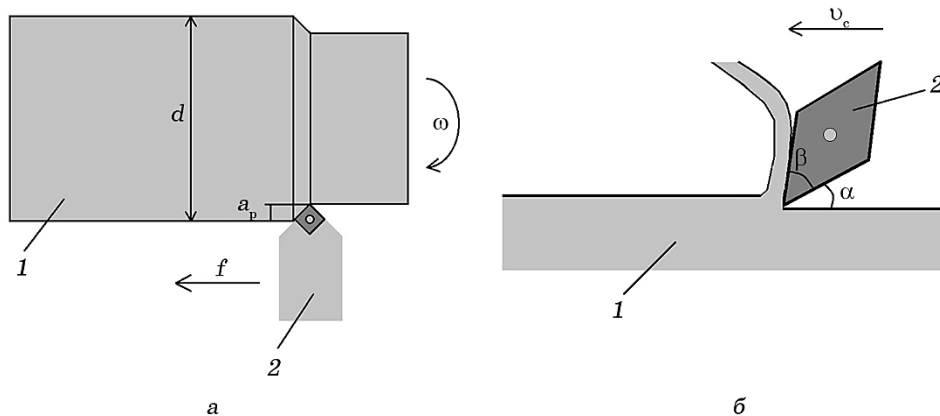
Параметри механічного оброблення заготовки з титану: 1 — заготовка з титану; 2 — різальний інструмент.
